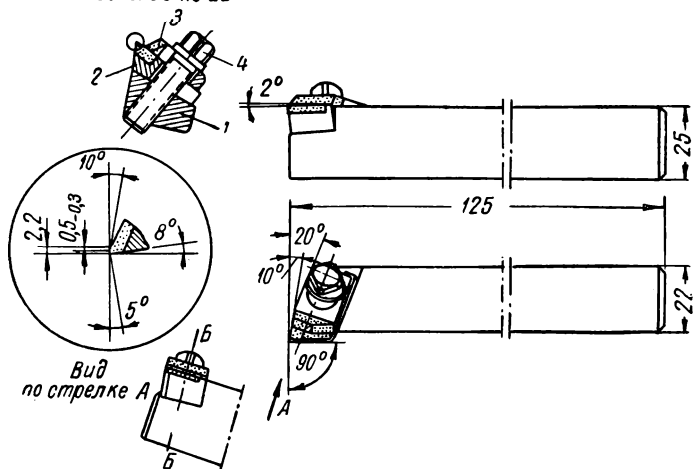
Проходной сборный резец с клиновидной сменной вставкой конструкции ВНИИ ( $\varphi = 45^\circ$ );
